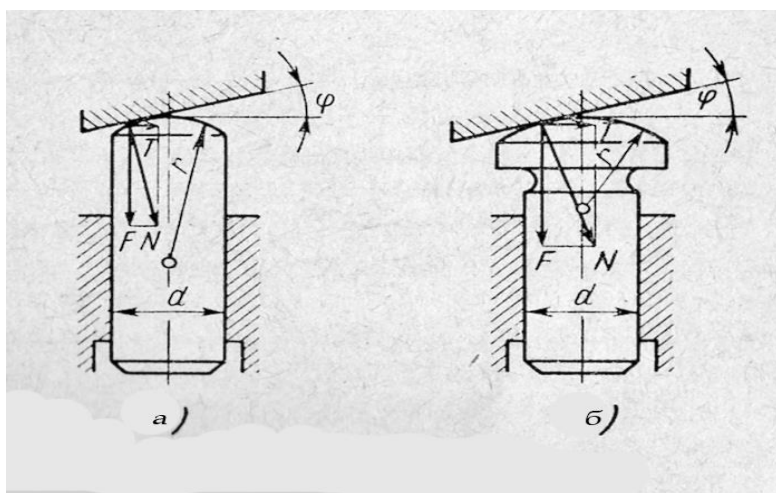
Схема контакта поршня со статорным кольцом, расположенным под углом.
